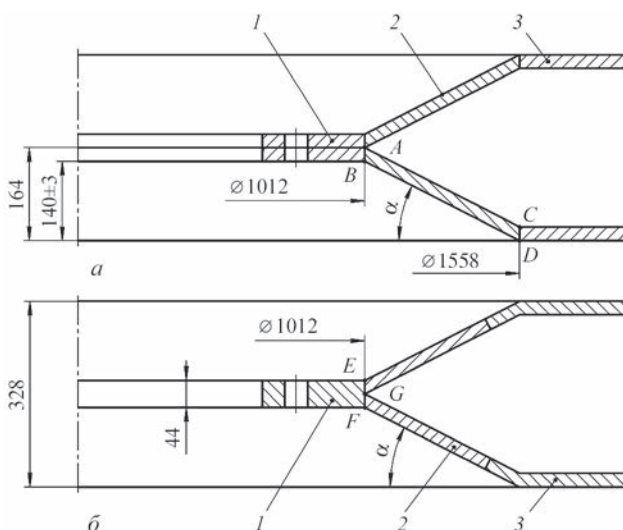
Первый (а) и второй (б) варианты выполнения сварного диска рабочего колеса дымососа: 1 — кольцо; 2 — обечайка; 3 — окантовка
